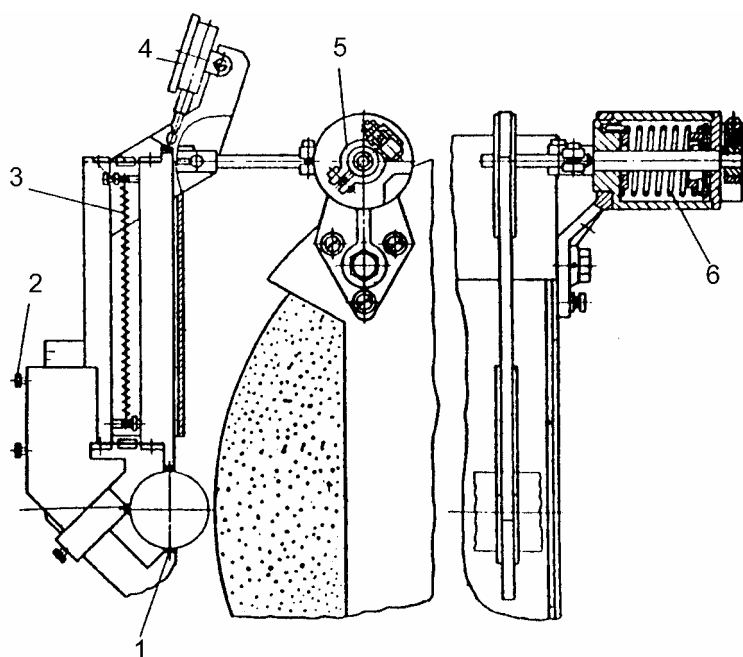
Скоба для измерения диаметра шеек валов при их шлифовании: 1 – опоры детали; 2 – винт; 3 – пружина; 4 – головка индикаторная; 5 – опора; 6 – пружина
